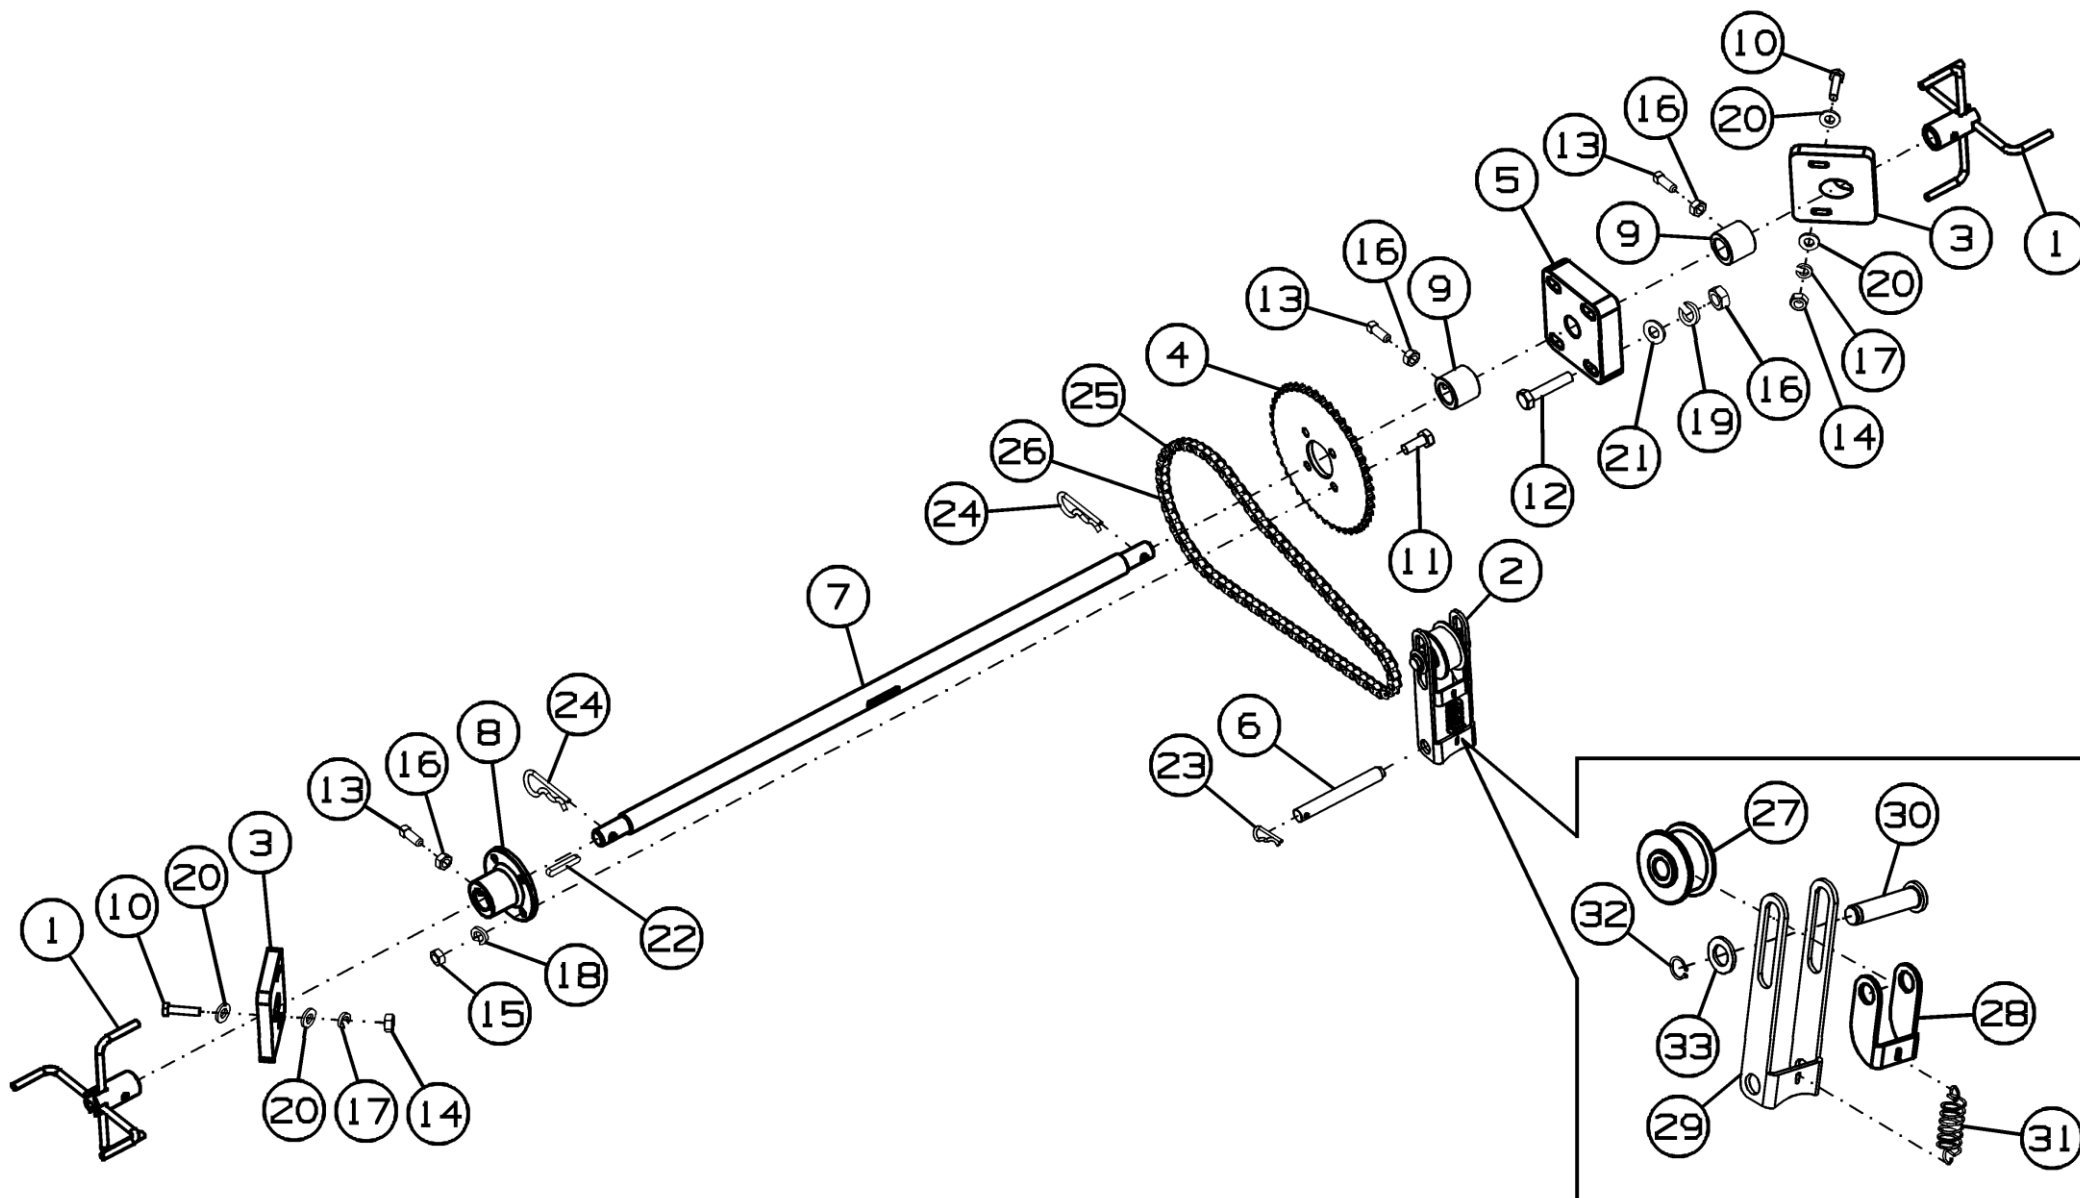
Установка воршилки РА-900.90.00.000Б
